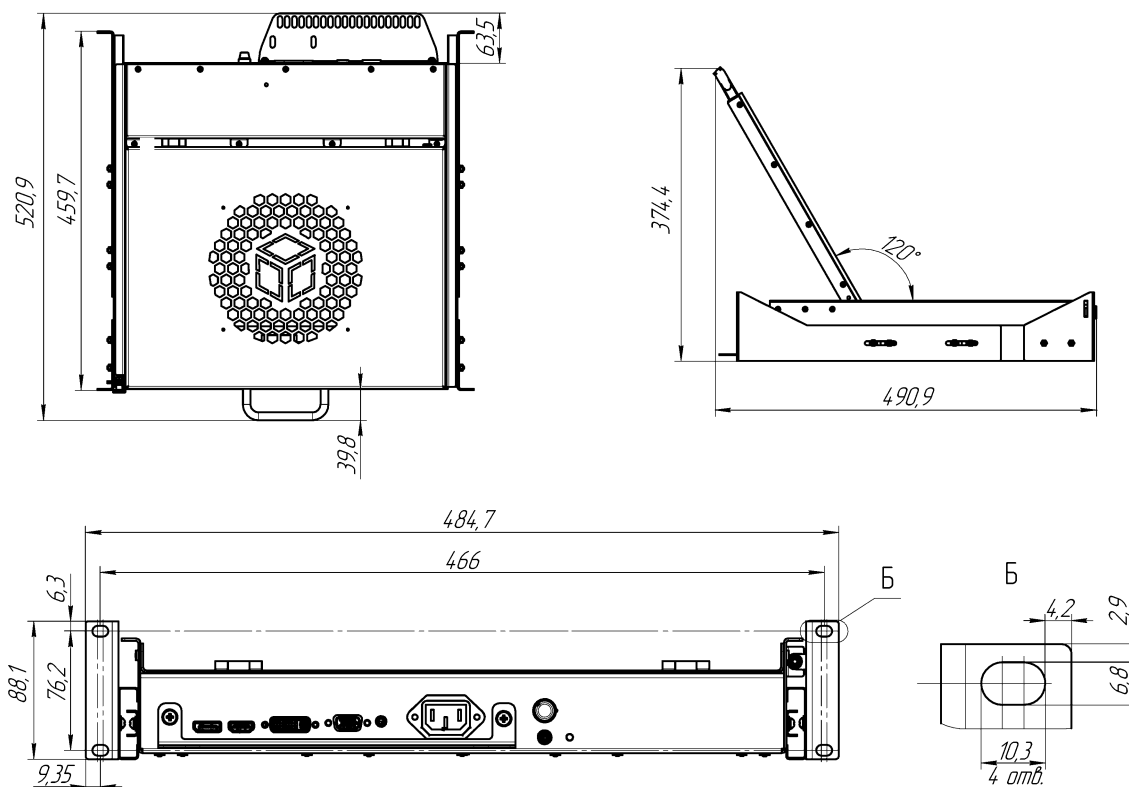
Габаритные и установочные размеры УУА-143-101
